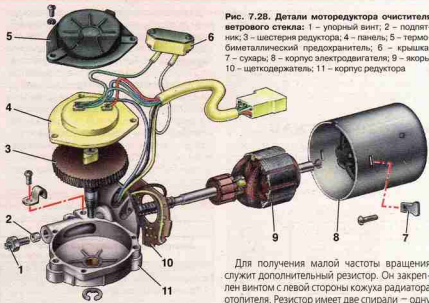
Детали моторедуктора очистителя ветрового стекла: 1 – упорный винт; 2 – подтяжка; 3 – шестерня редуктора; 4 – панель; 5 – термометаллический предохранитель; 6 – крышка; 7 – ось; 8 – корпус электродвигателя; 9 – якорь; 10 – щеткодержатель; 11 – корпус редуктора
